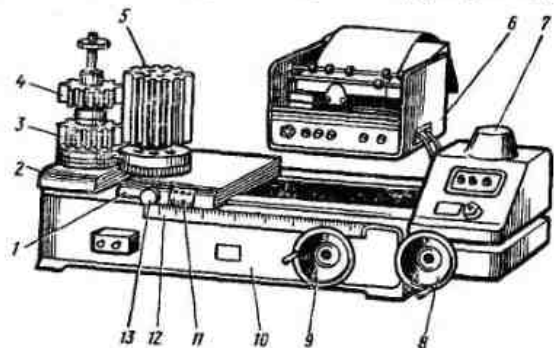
Прибор для измерения кинематической погрешности зубчатых колес
